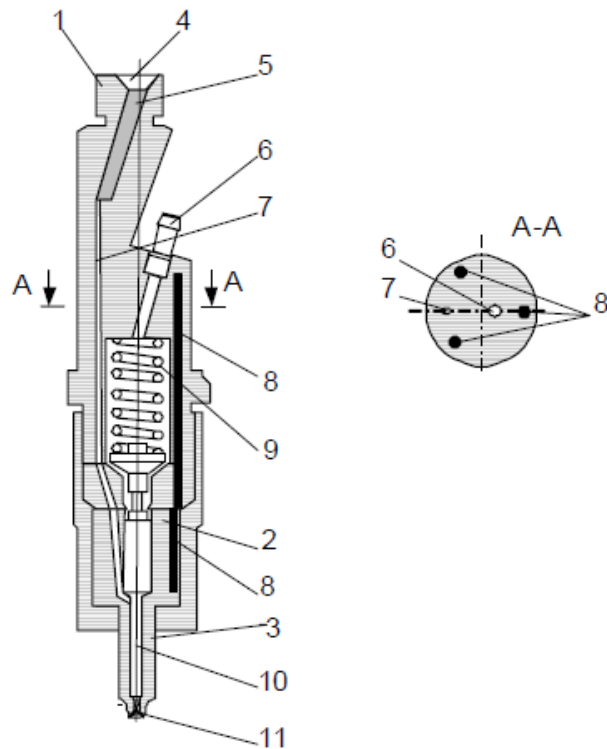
Схема розпилювача з підігрівом палива для роботи на рапсовому маслі: 1 - корпус форсунки; 2 - розпилювач; 3 - корпус розпилювача; 4 – вхідний штуцер; 5 - паливний фільтр; 6 - відвідний штуцер; 7 – паливopідводчий канал; 8 - нагрівальний елемент; 9 - пружина; 10 - голка розпилювача; 11 - розпилюють отвори
